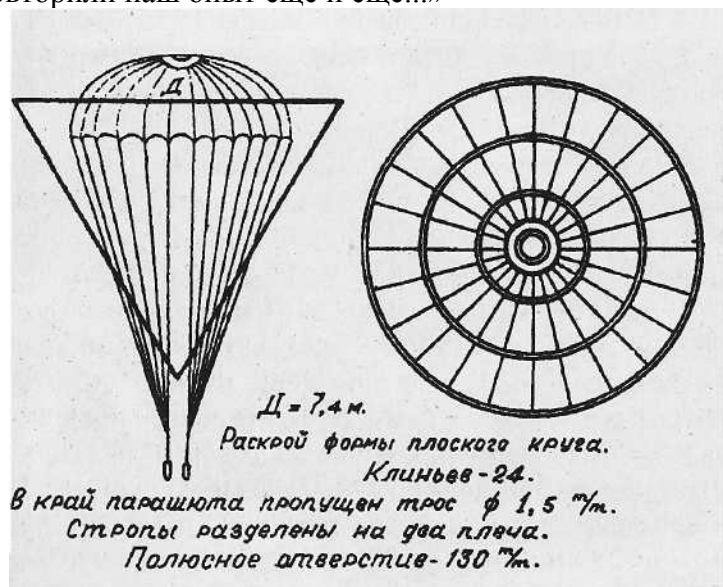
Первый русский парашют образца 1911. Чертеж Г.Е. Котельникова
